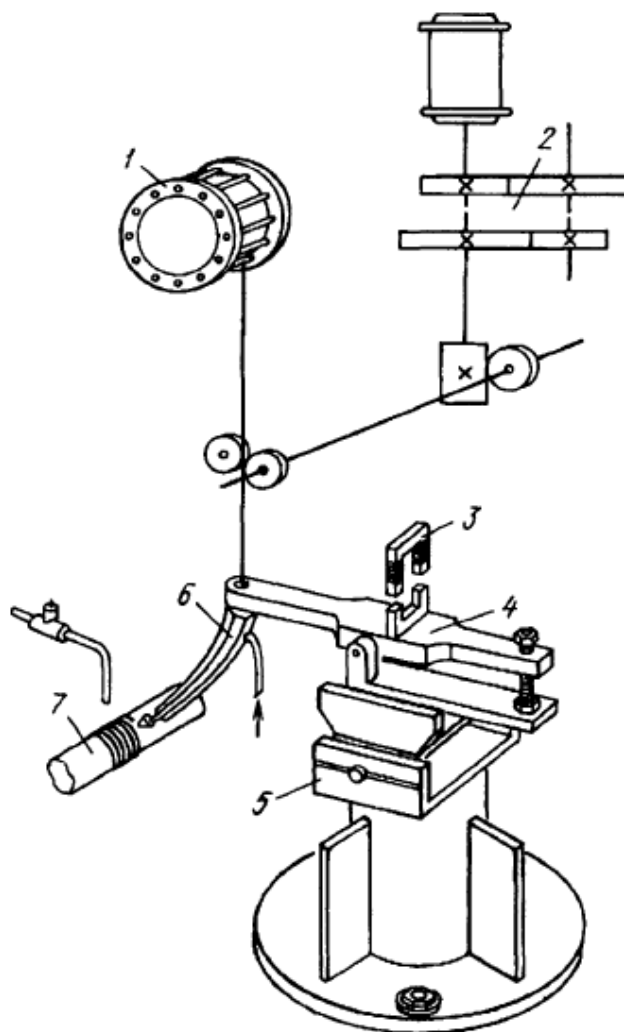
Схема вибродуговой установки конструкции ЧТЗ
